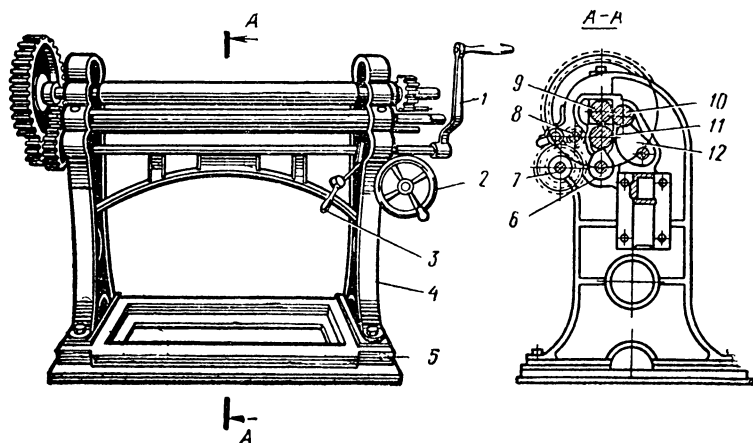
Листогибочный трехвалковый станок с ручным приводом:
